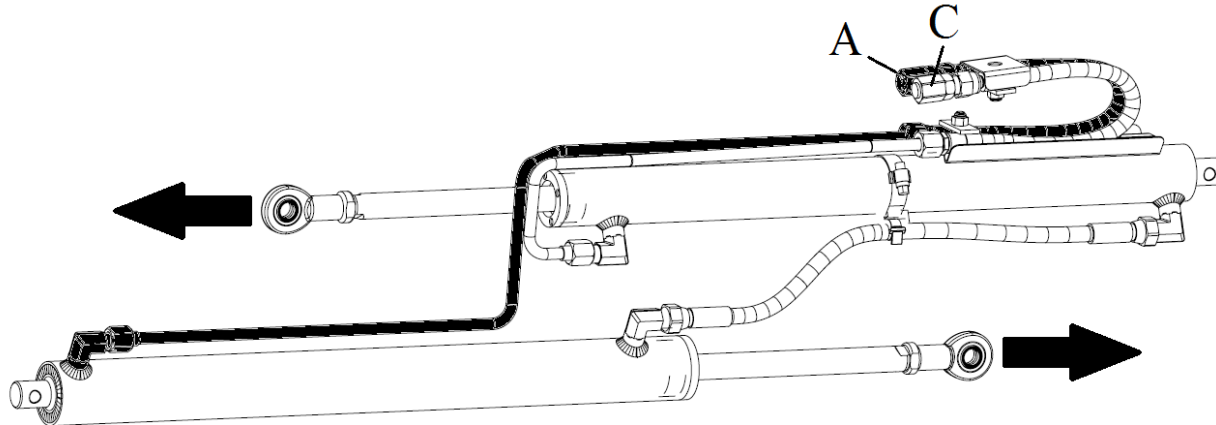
Hydraulische Anlage für die Ausführungen ohne Seitenschub und mit Position der Zinkenversorgungsingänge im Inneren des Rahmens.
